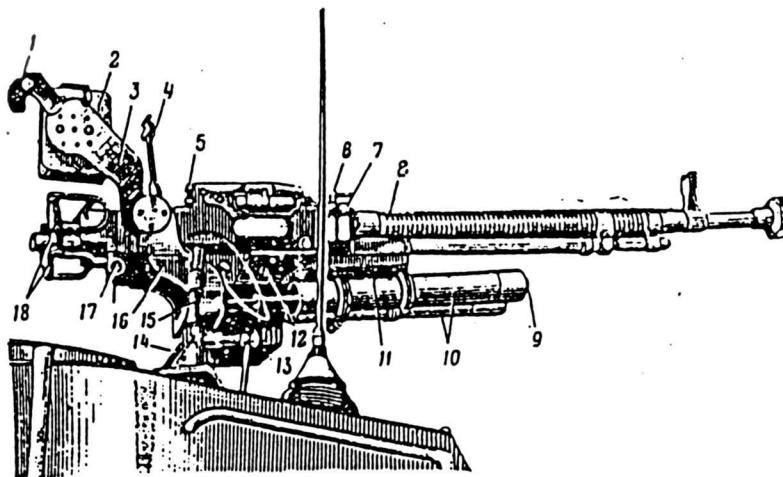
Зенитная установка 12,7-мм пулемета ДШК (вид справа):
